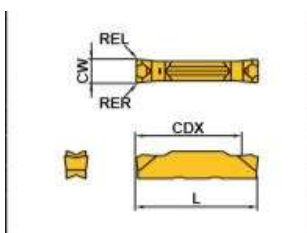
Пластина Mitsubishi для получения канавки
